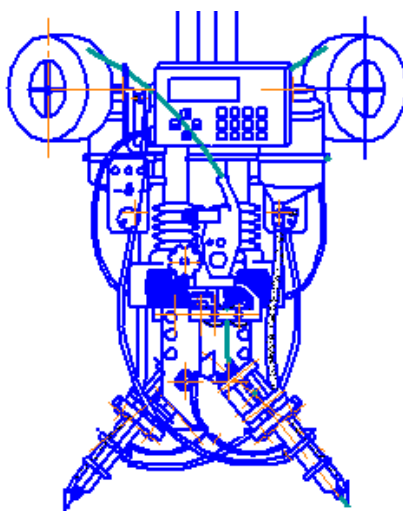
Сварочный автомат АДГ-630
